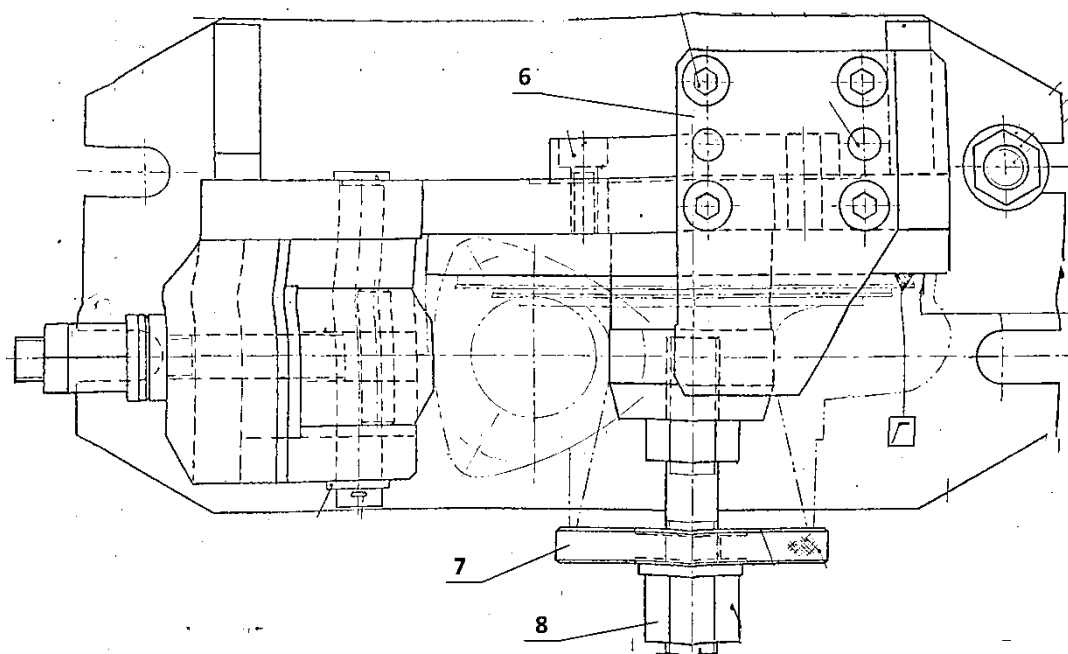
Приспособление фрезерное. Вид сверху: 6 – Установ, 7 – Упорная шайба, 8 – Гайка.
